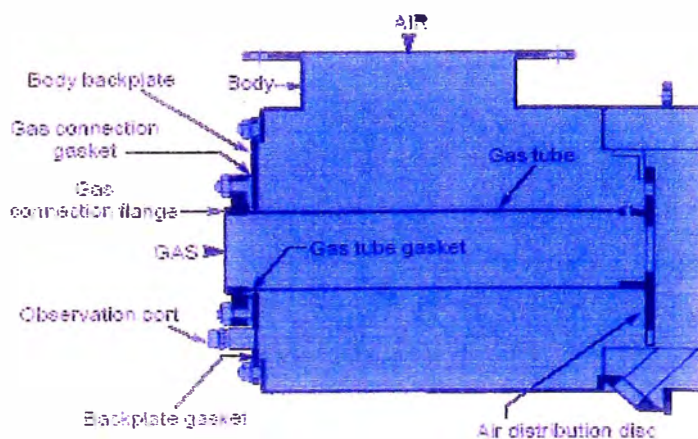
Quemador Nozzle Mix con ingreso axial de gas
